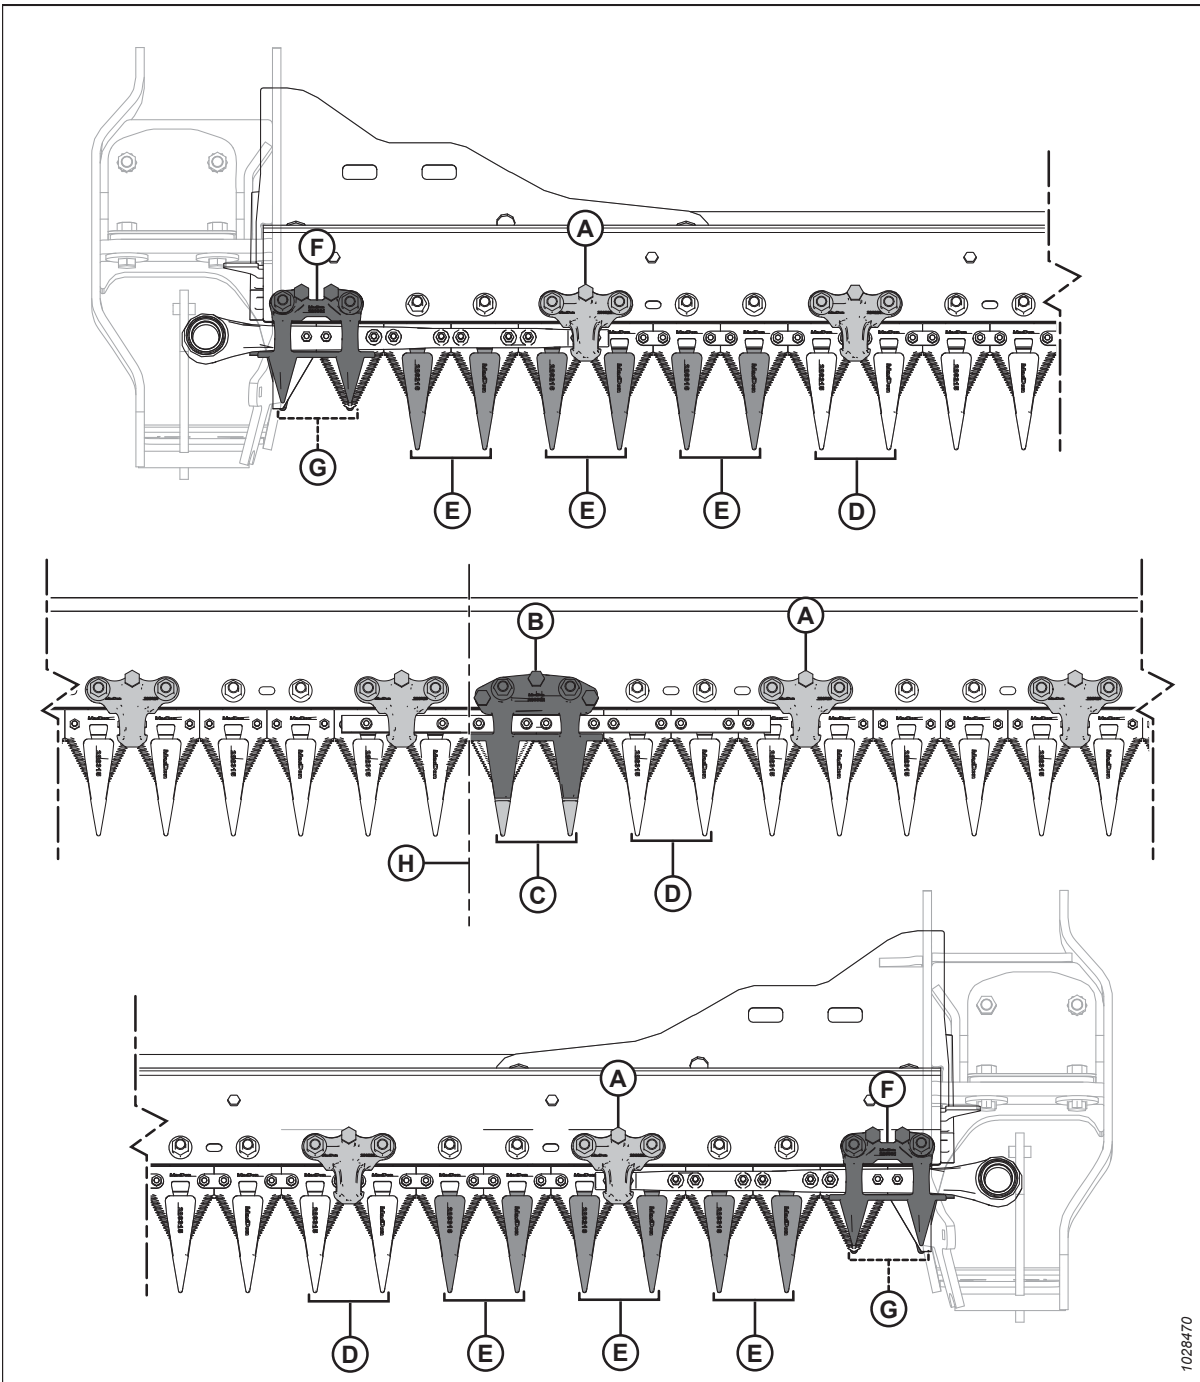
Emplacement des doigts de couteaux pointus et mécanismes de retenue
